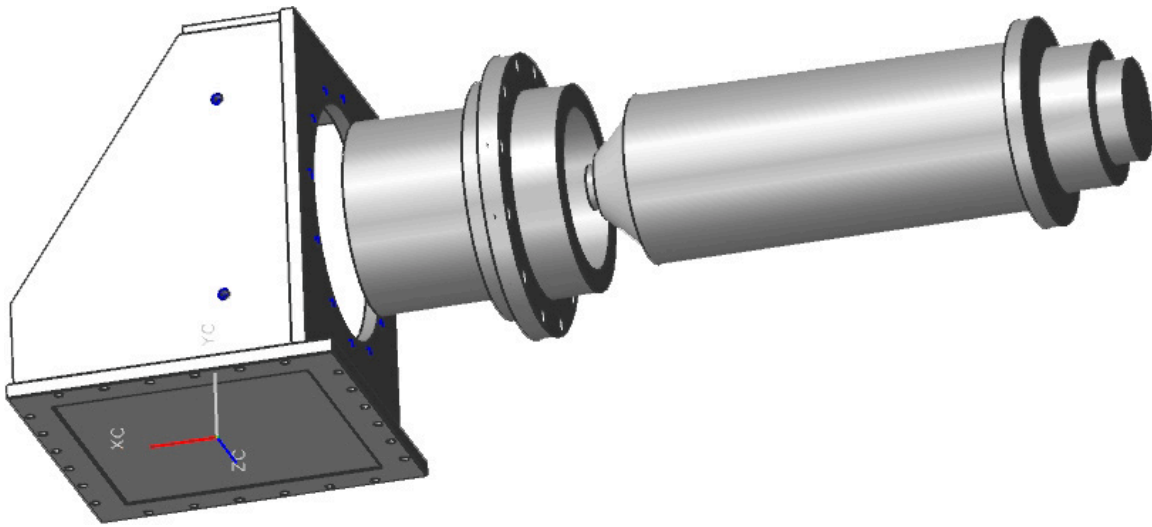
Explosionsansicht der Spindeleinheit. Die Werkzeugspindel wird von einer zylindrischen Spindelhülse gehalten, die wiederum mit dem Spindelkasten verschraubt wird.
